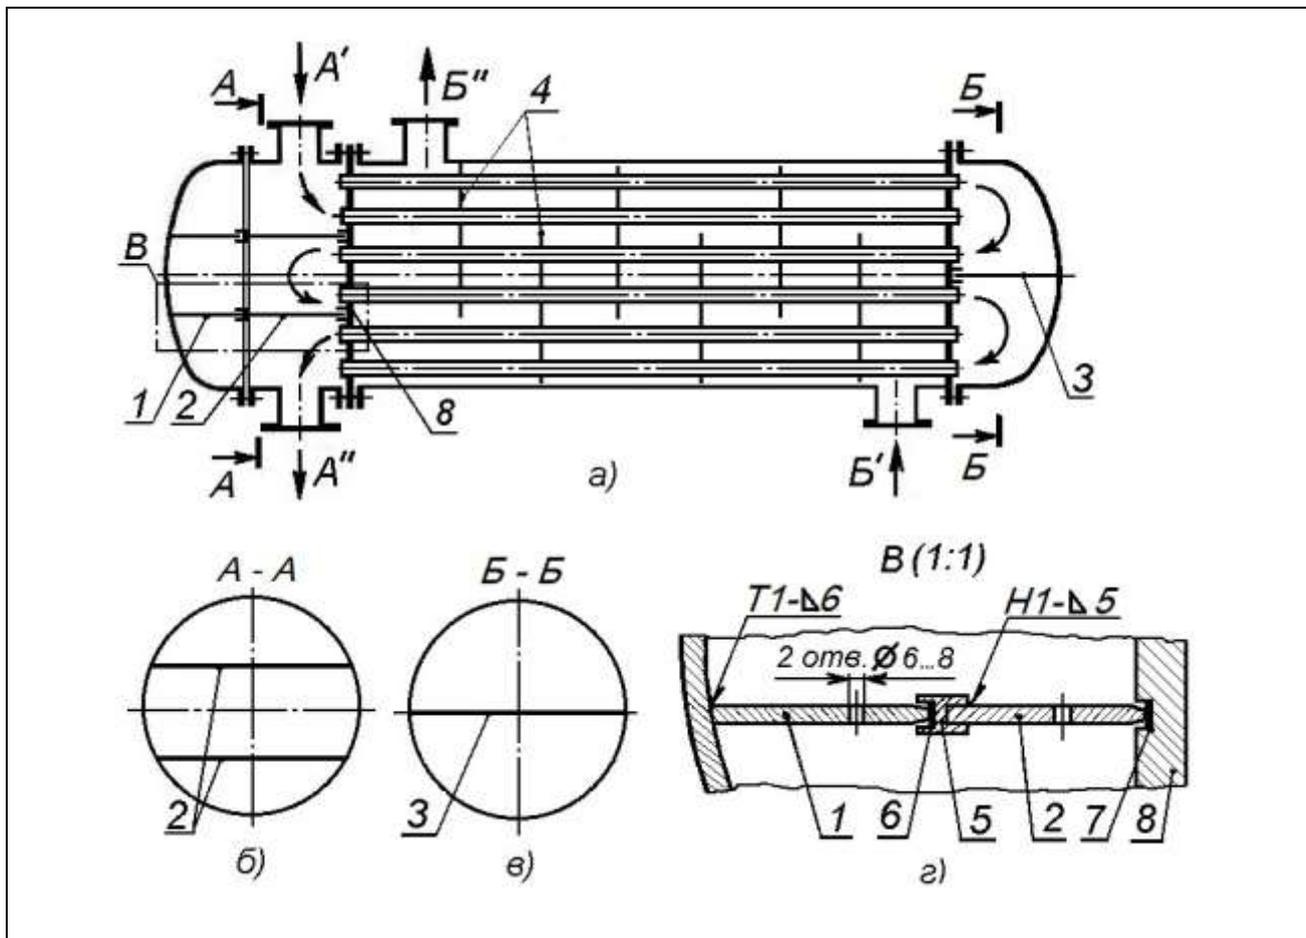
Теплообменники с продольными хордовыми 1, 2, 3 и поперечными 4 перегородками: а) – общий вид; б), в) – схемы размещения хордовых продольных перегородок 1, 2 и 3 на крышках; з) – схема соединения продольных перегородок 1 и 2 методом сварки с крышкой и с прокладкой 7 с трубной решеткой 8
